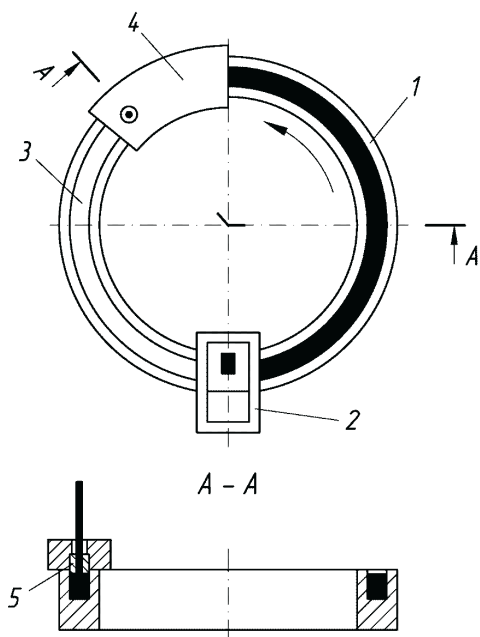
Схема установки непрерывного литья-прессования с вертикальной осью вращения колеса-кристаллизатора: 1 – рабочее колесо (кристаллизатор); 2 – литниковая коробка; 3 – кольцевая канавка; 4 – башмак; 5 – матрица для прессования
